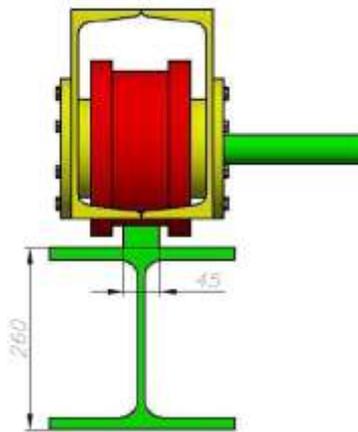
Rueda de tracción apoyada sobre la viga carrilera. Fuente: (Autor)
